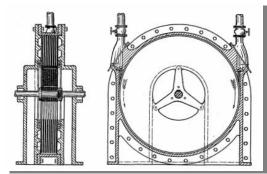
Diseño de la turbina sin álabes de Tesla.
